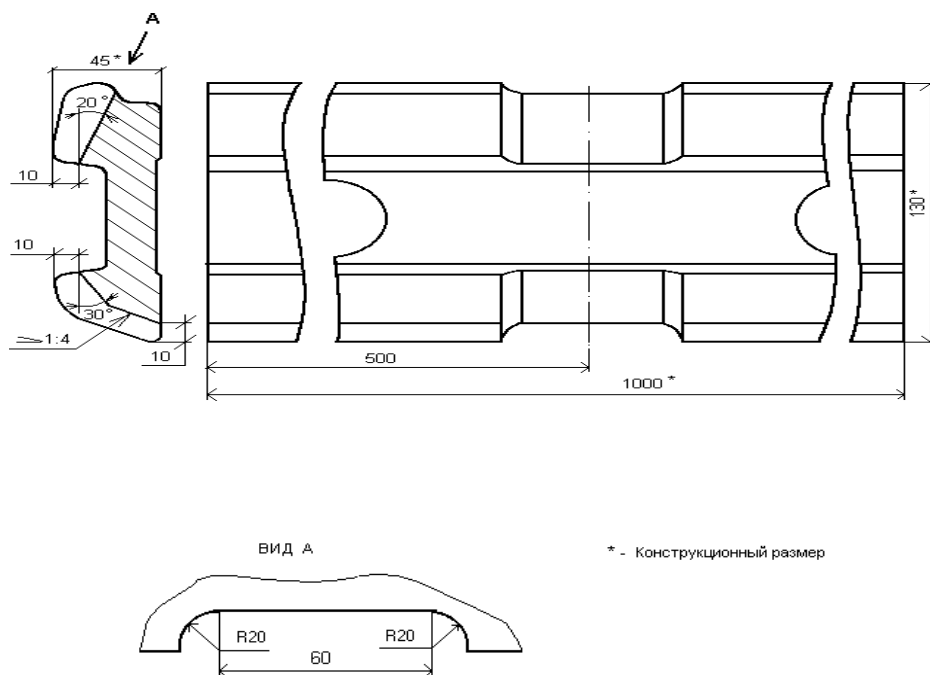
Специальная накладка для укрепления термитного стыка с дефектом
